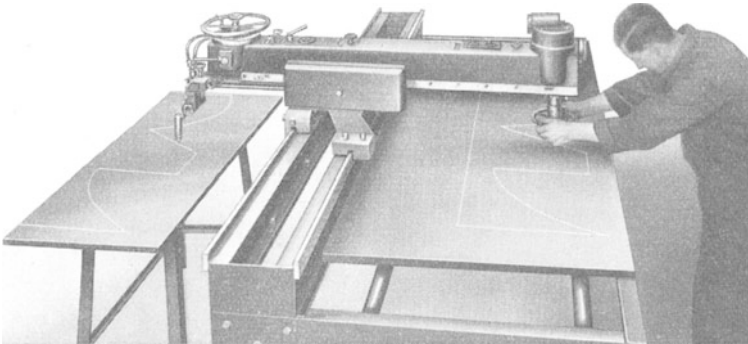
Schwere Universalschneidmaschine mit Querwagen.
